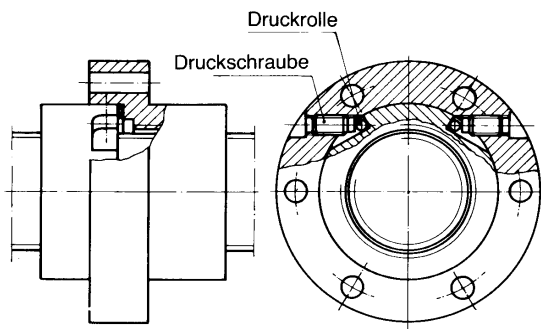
Flanschmutter mit Vorspannvorrichtung
